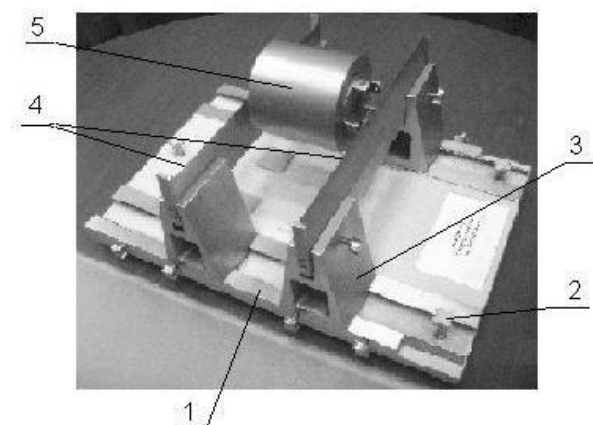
Ножевая опора для статической балансировки подвижных узлов приборов:
